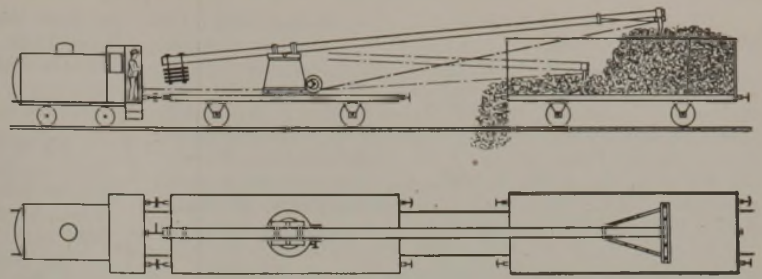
Einrichtung zum Ausladen bauschiger Schüttgüter.
